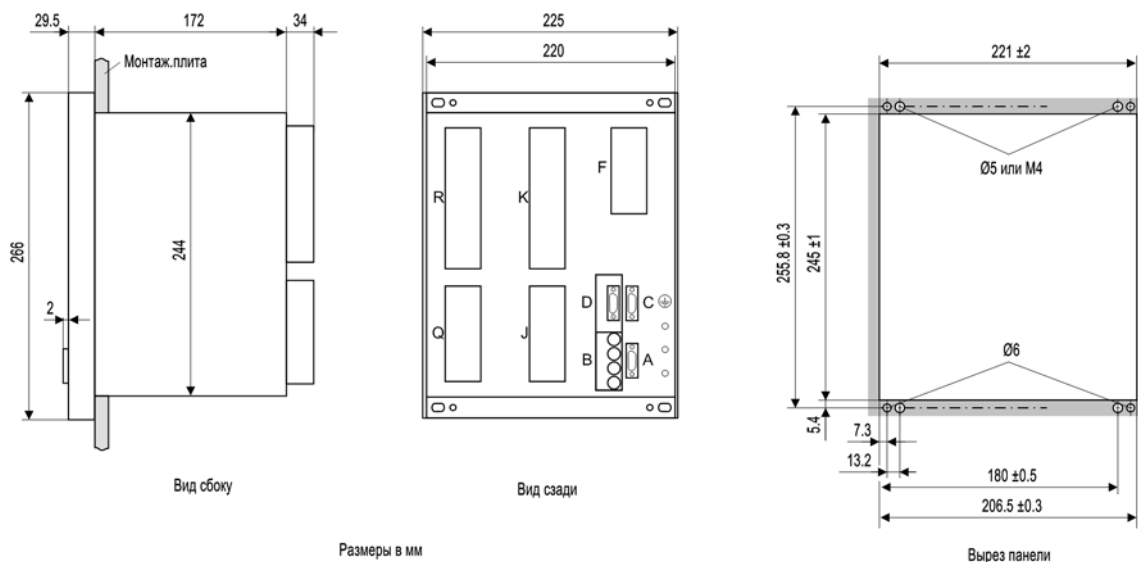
Размеры устройства для утопленного монтажа на панели и в шкафу (размер корпуса $1/2$)
